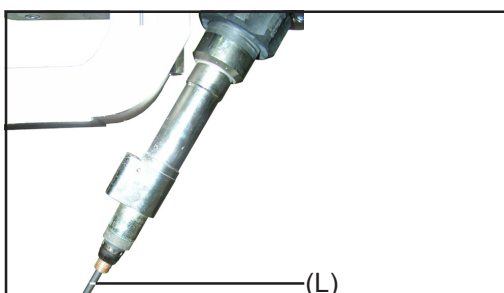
Drahtführungsseele Schweißbrenner einbauen
